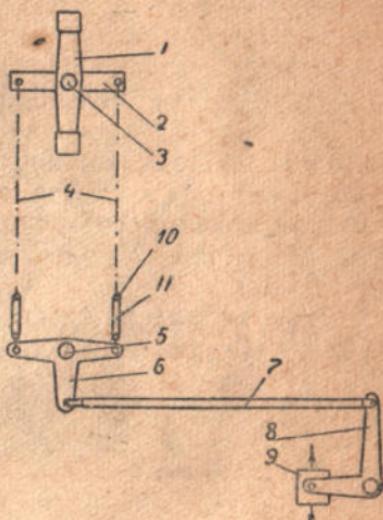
Схема управления реверсивного механизма по-ворота стрелы.
